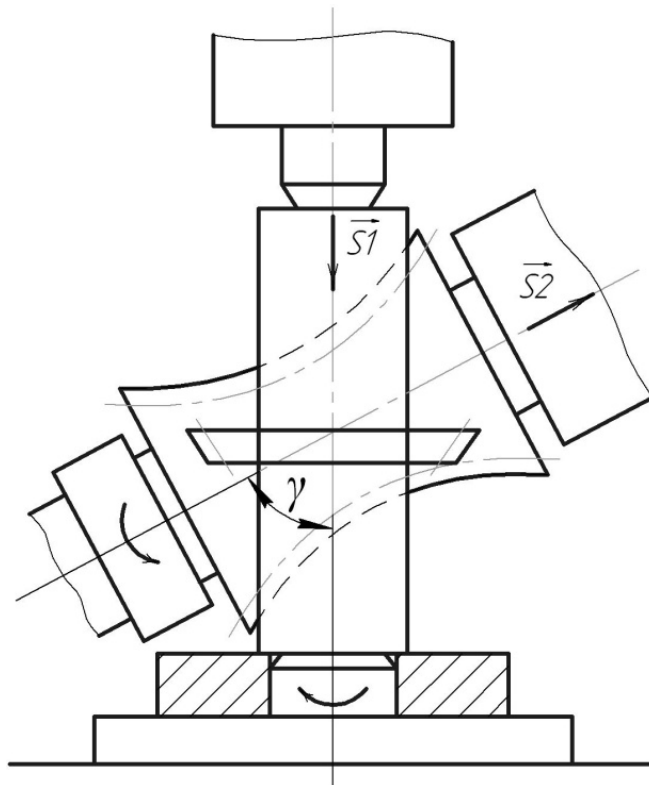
Схема изготовления винтовых зубчатых колёс
